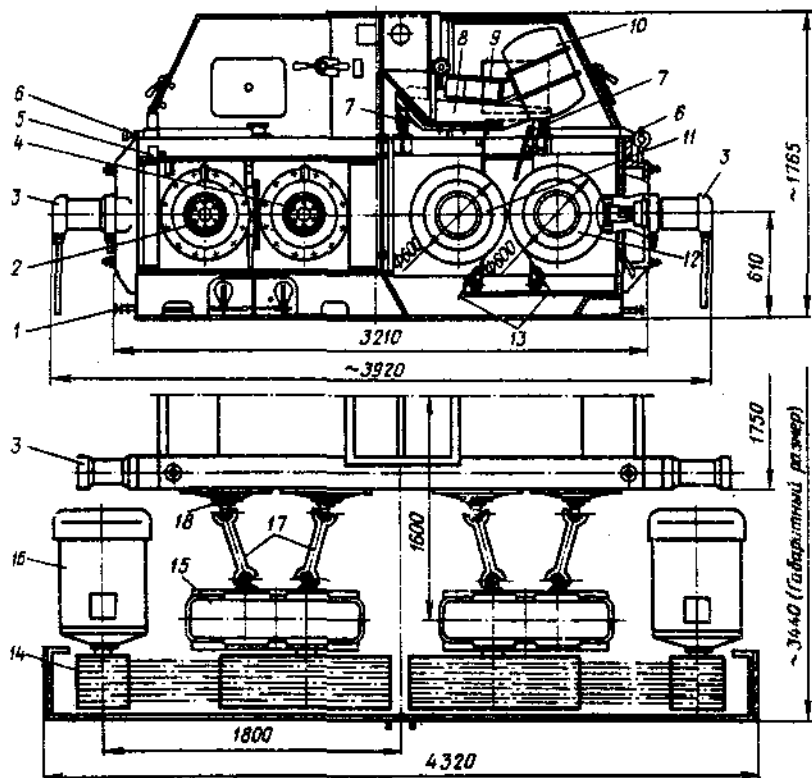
Двухпарный плющильный вальцовый станок ФВ-600
